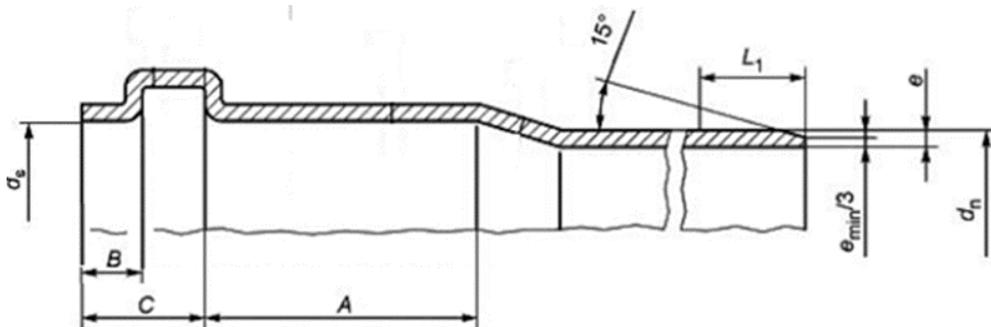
Основные размеры раструба и трубного конца под уплотнительное кольцо.
